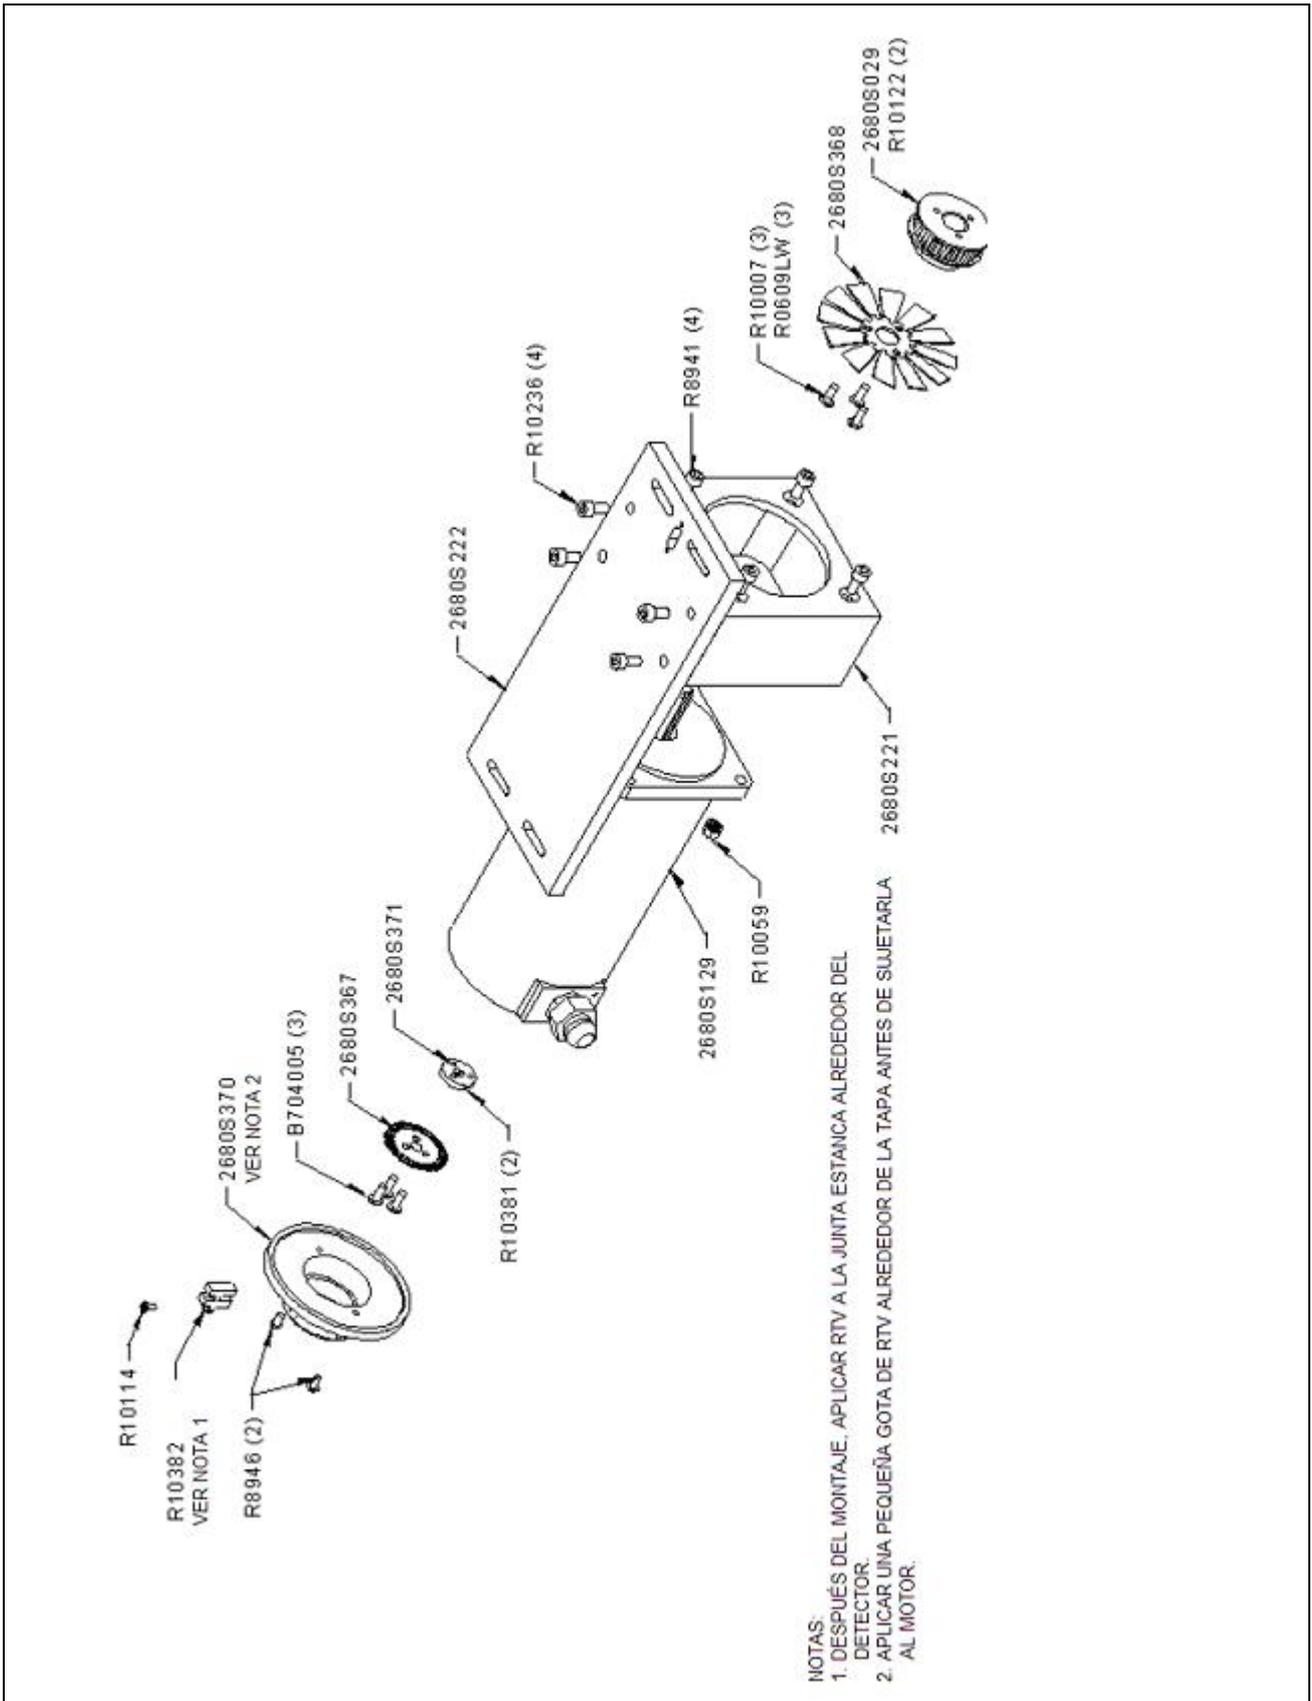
Dibujo de despiece de la parte central de la torreta del disco de corte (2780S805).
